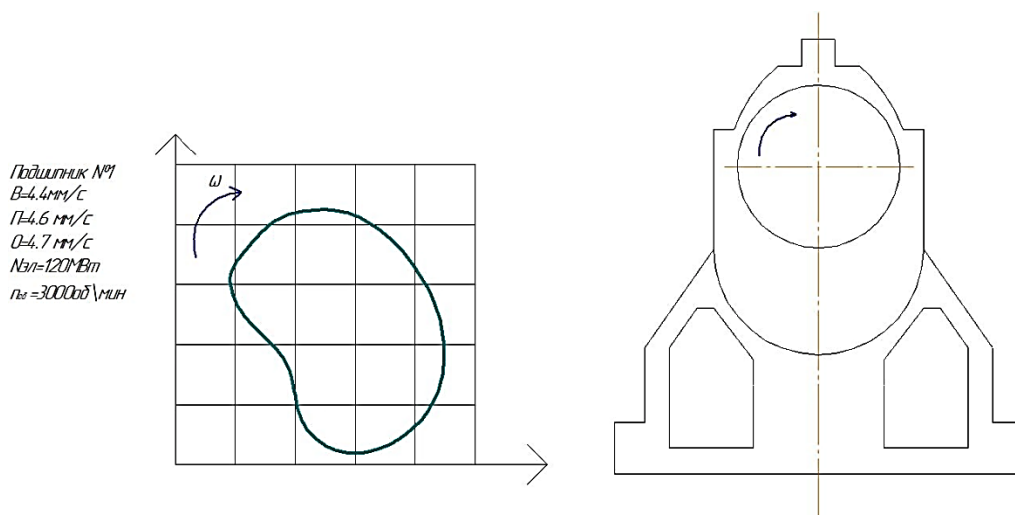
Модель движения шейки вала внутри подшипника № 1 с 01.04.23 г. по 01.05.23 г.
